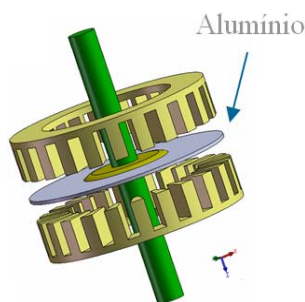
Desenho do motor em disco com o rotor em alumínio.
